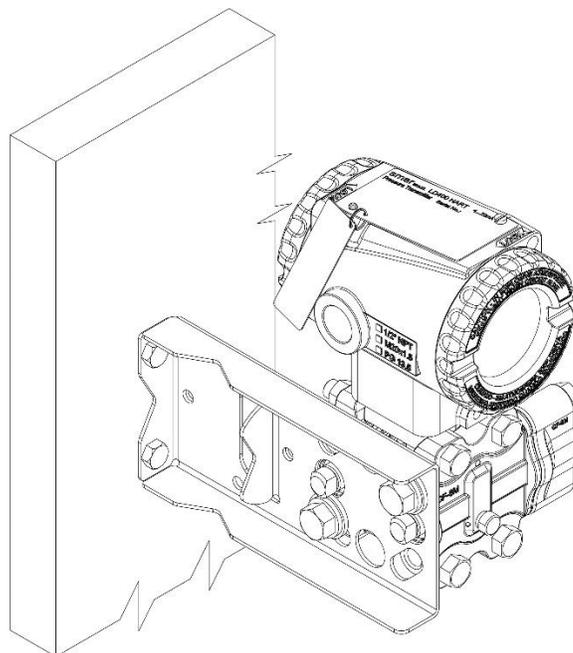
Desenho de Montagem do LD400 HART em Painel ou Parede
